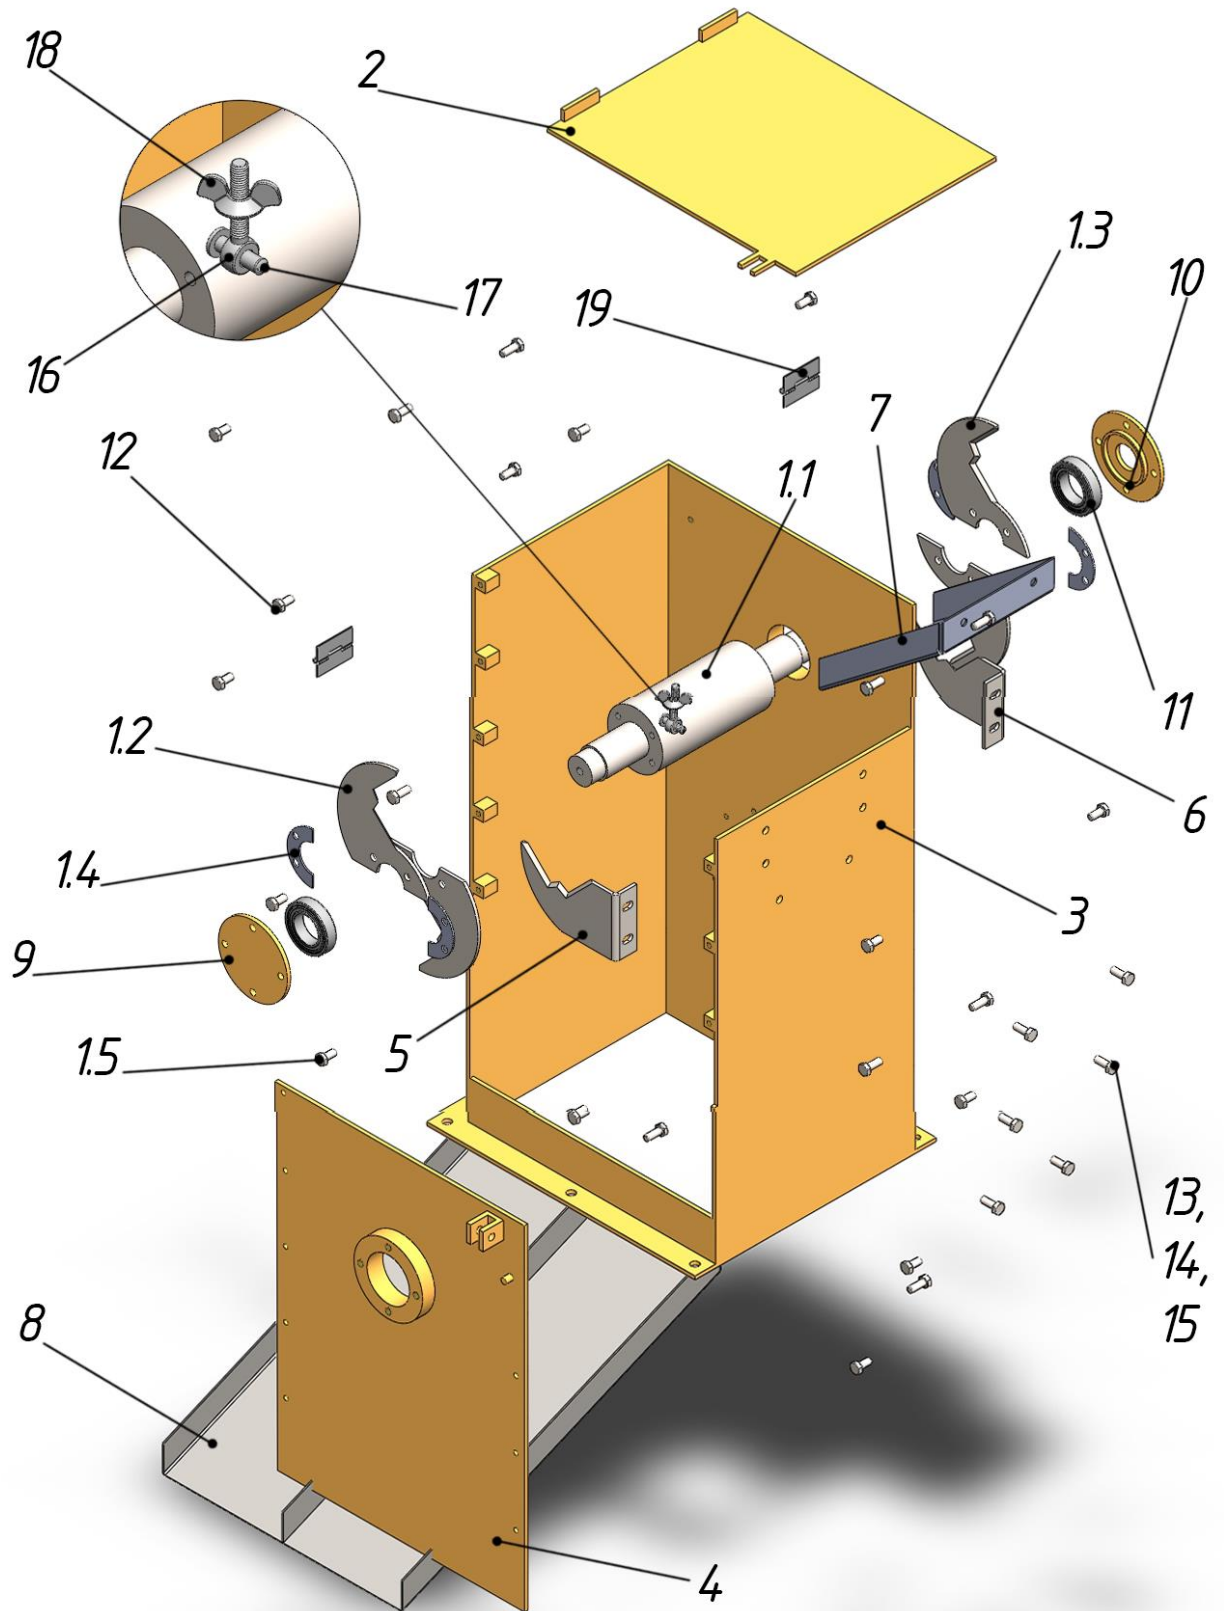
Вид робочого вузла з рознесеними частинами
